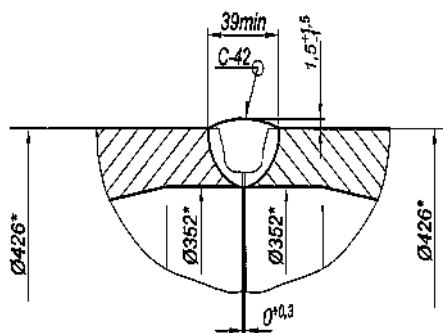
Схема сварного соединения трубопровода
